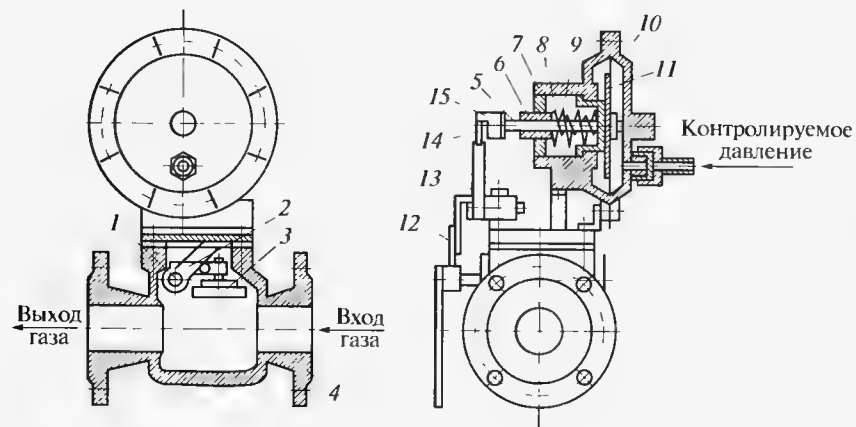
Предохранительно-запорный клапан КПЗ:
